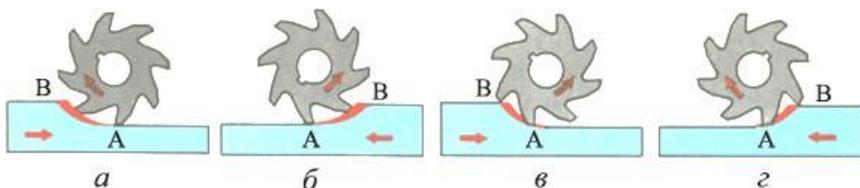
Схеми обробки поверхонь заготовок на горизонтально- та вертикально-фрезерних верстатах
